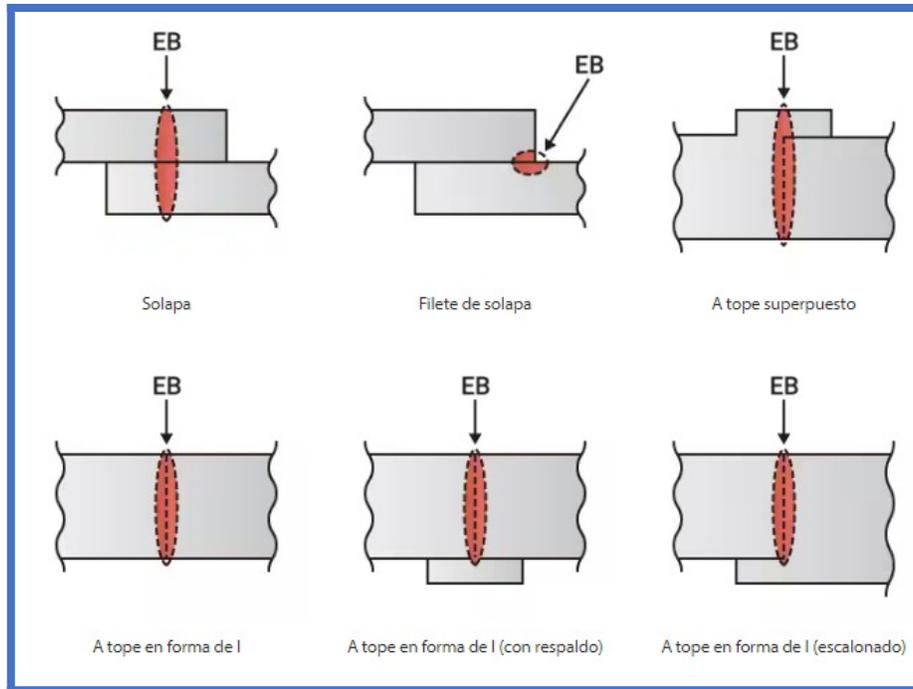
A y B Uniones de soldadura típicas posibles con la soldadura por haz de electrones (EB = HAZ DE ELECTRONES)
